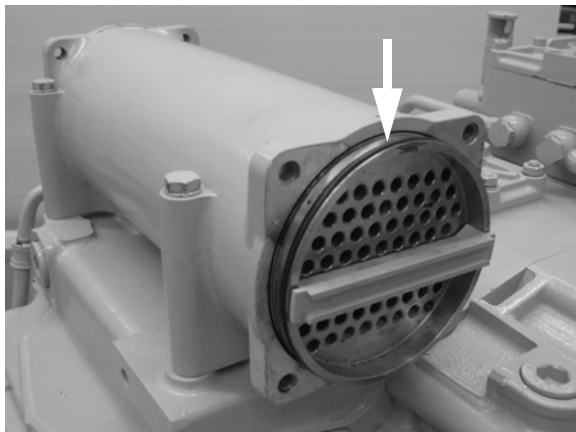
Auf den äußeren O-Ring beim Einbau achten (Beispiel)
